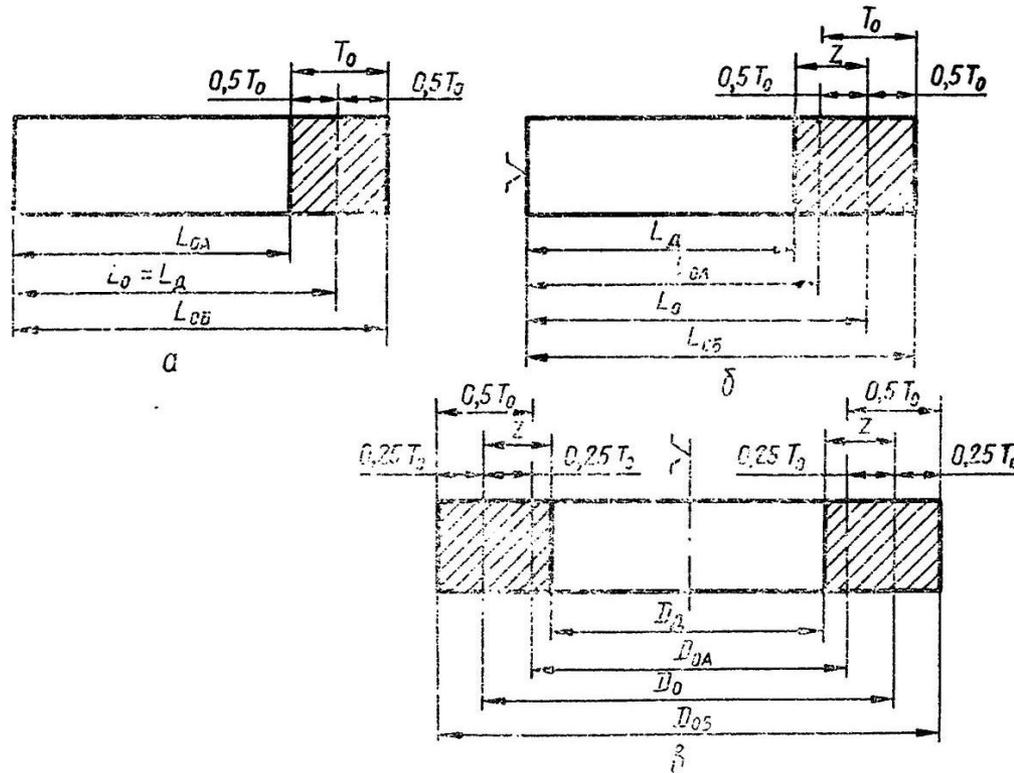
Взаимосвязь между номинальными размерами детали и отливки: а – размер до необрабатываемой поверхности детали; б – размер до обрабатываемой поверхности при обработке каждой поверхности отливки от своей базы; в – размер до обрабатываемой поверхности при обработке противоположных поверхностей, симметричных (или тел вращения) отливок от общей базы; L_d , D_d – номинальные размеры детали; L_o , D_o – номинальные размеры отливки; L_{oa} , D_{oa} – наименьший размер отливки; $L_{об}$, $D_{об}$ – наибольший размер отливки; T_o – допуск отливки; Z – средний припуск на механическую обработку
